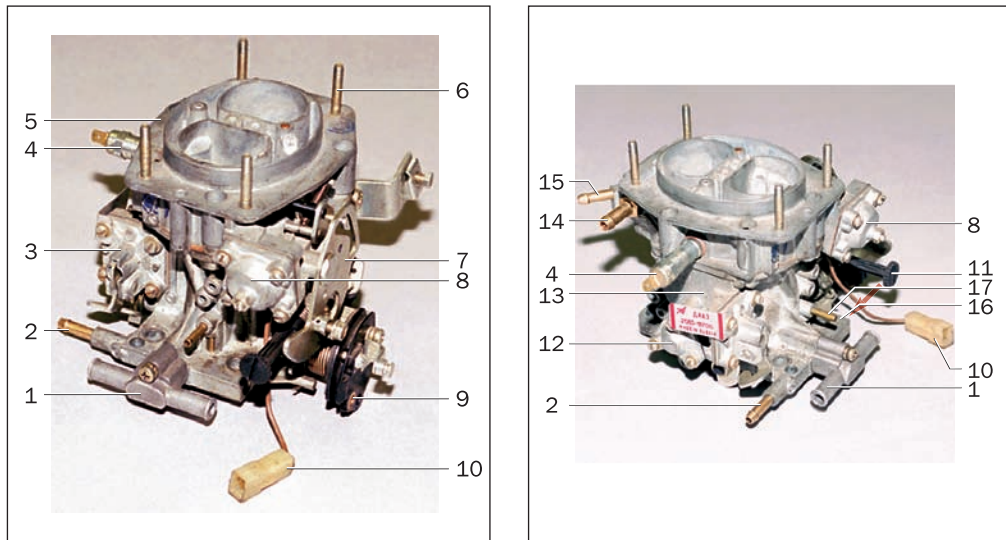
Внешний вид карбюратора: 1 — блок подогрева зоны дроссельной заслонки; 2 — штуцер вентиляции картера двигателя; 3 — крышка ускорительного насоса; 4 — электромагнитный запорный клапан; 5 — крышка карбюратора; 6 — шпилька крепления воздушного фильтра; 7 — рычаг управления воздушной заслонкой; 8 — крышка пускового устройства; 9 — сектор рычага привода дроссельных заслонок; 10 — колодка провода датчика-винта ЭПХХ; 11 — регулировочный винт количества смеси холостого хода; 12 — крышка экономайзера; 13 — корпус карбюратора; 14 — штуцер подачи топлива; 15 — штуцер отвода топлива; 16 — регулировочный винт качества смеси холостого хода (по стрелке); 17 — штуцер для подачи разрежения к вакуумному регулятору зажигания
